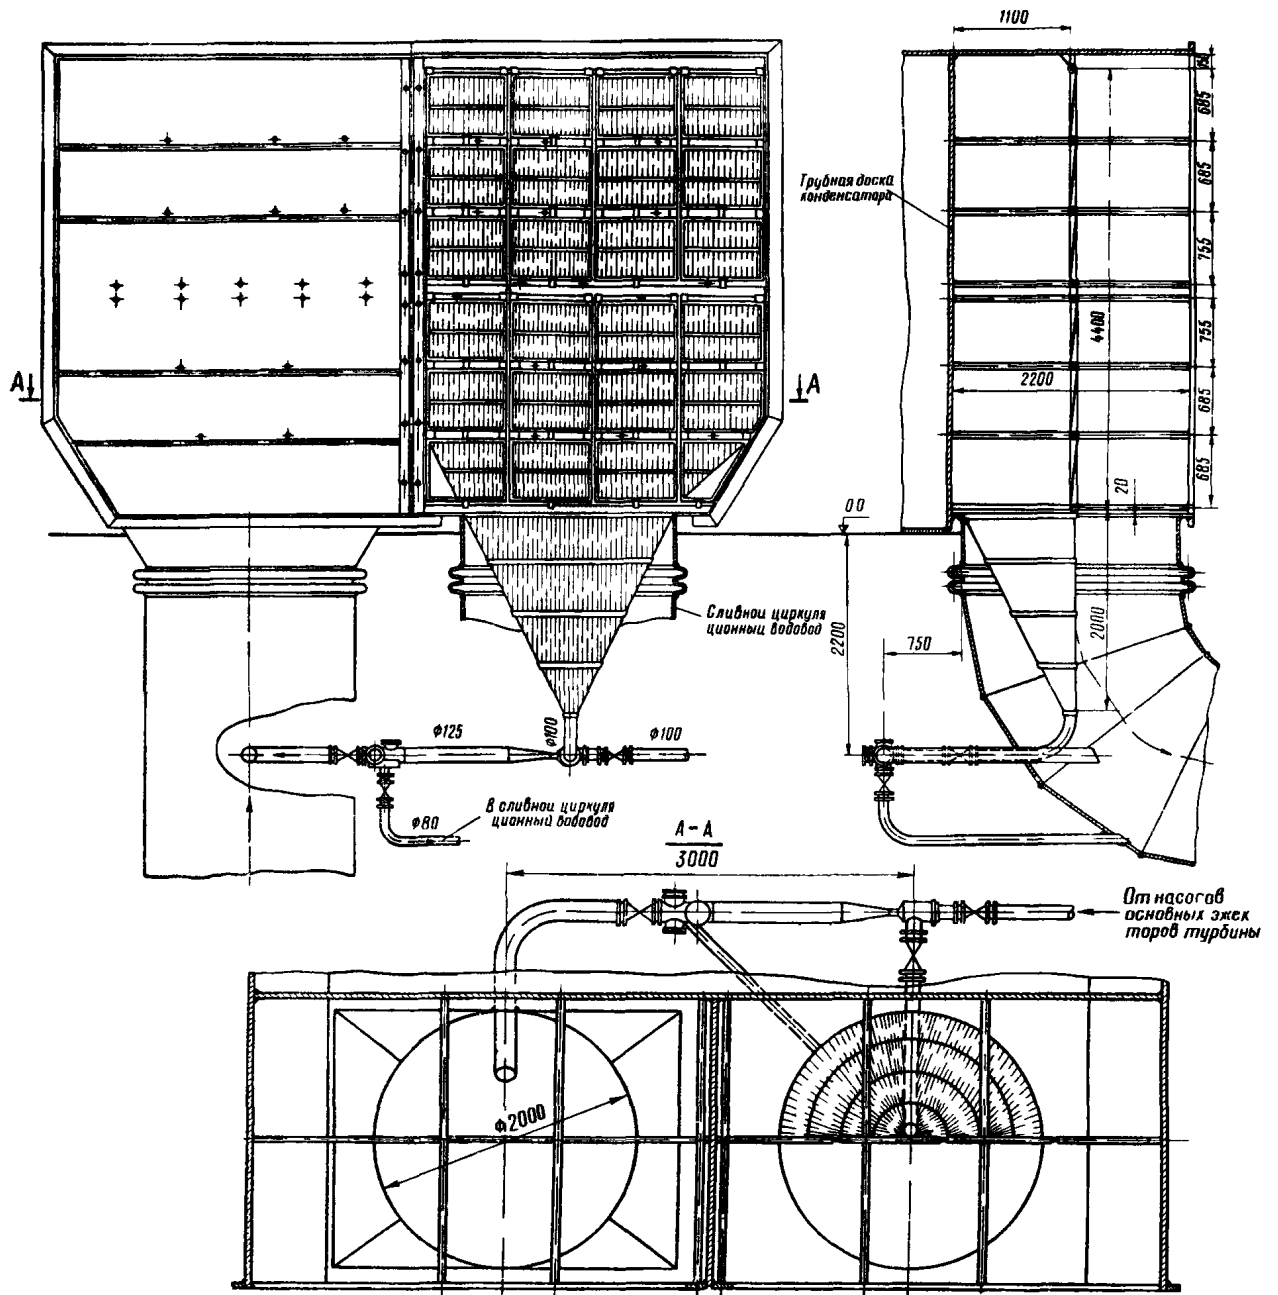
Монтажная схема установки непрерывной очистки конденсатора турбины К-800-240 ДМЗ резиновыми шариками
